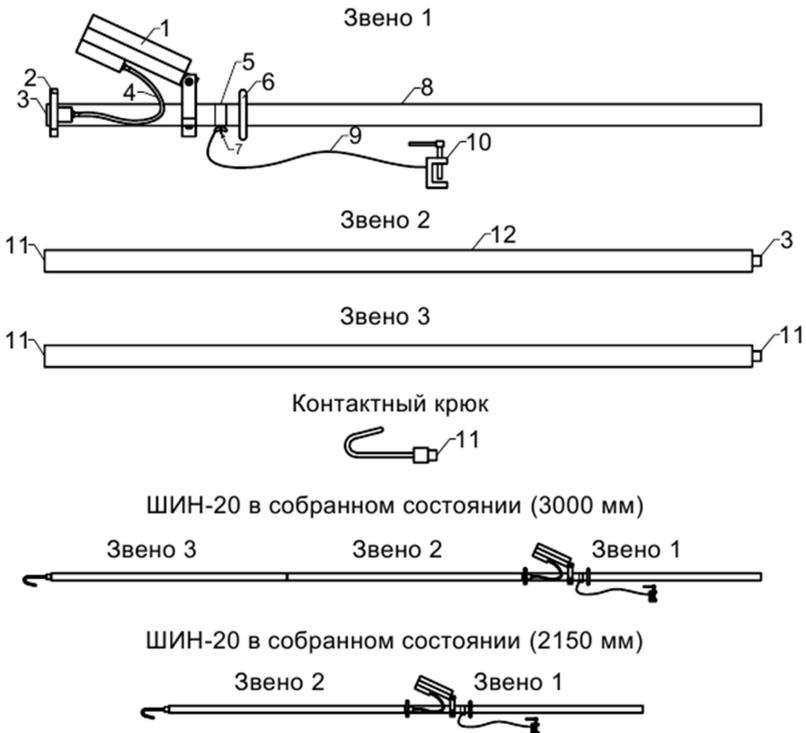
Внешний вид штанги-измерителя наведенного напряжения ШИН-20:
